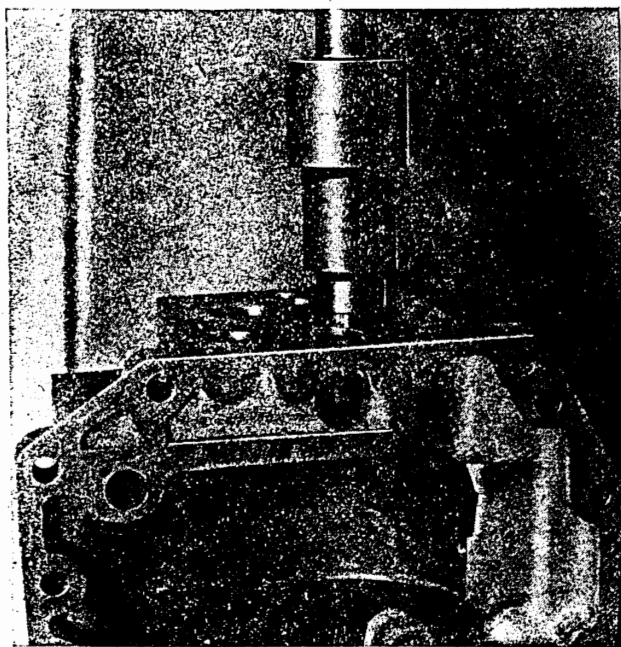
Eindringen der Ölpumpenachse in das Antriebsgehäuse mittels Handhebelpresse
